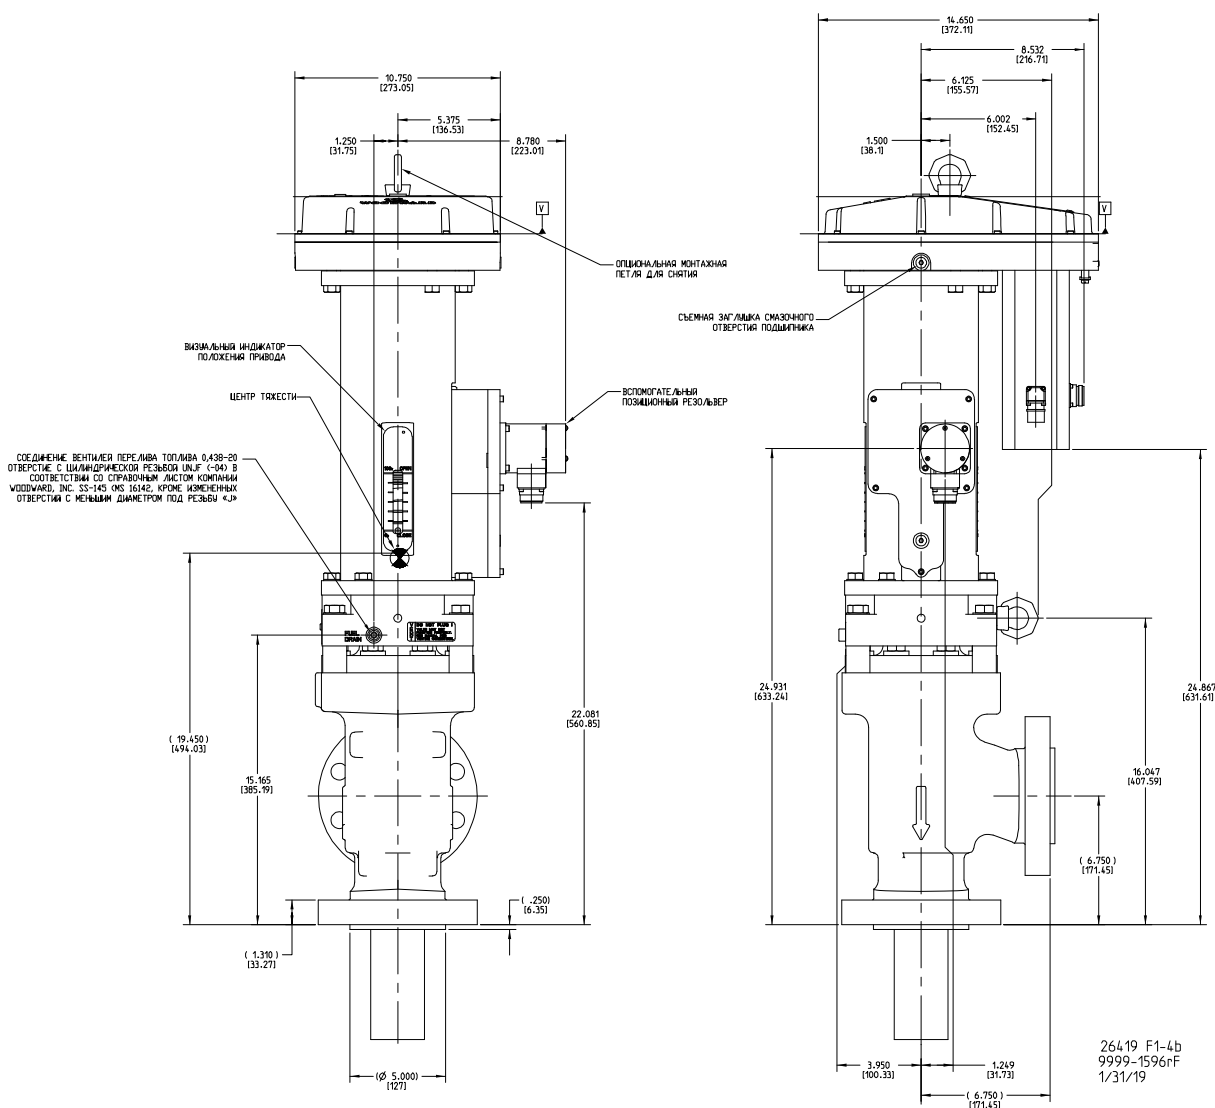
Габаритный чертеж (3-дюймовый клапан LESV класса 600)
